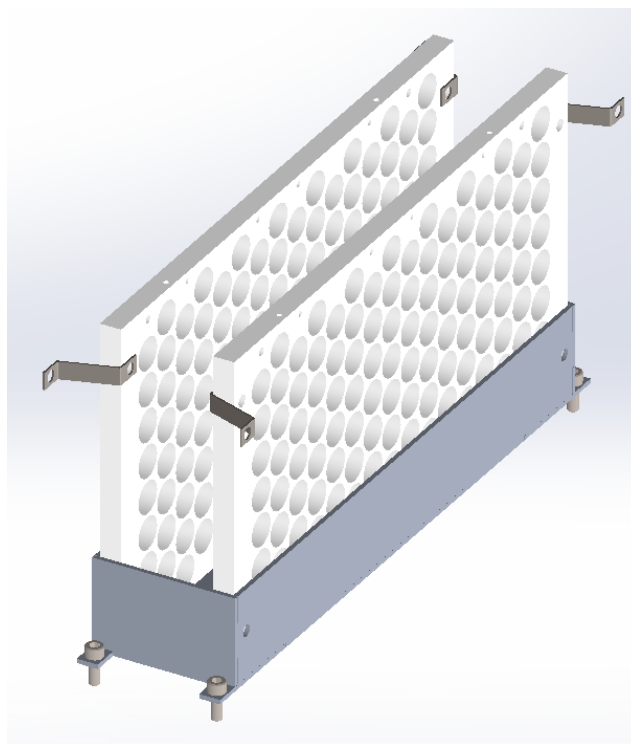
Soportes y puntos de anclaje del módulo de celdas
